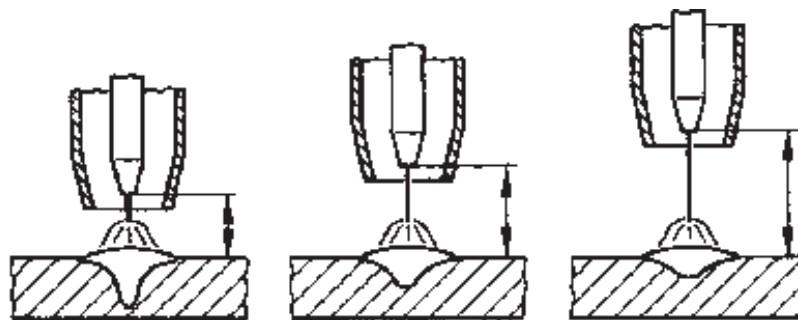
Efecto de diferentes longitudes libres del electrodo sobre el cordón de soldadura
